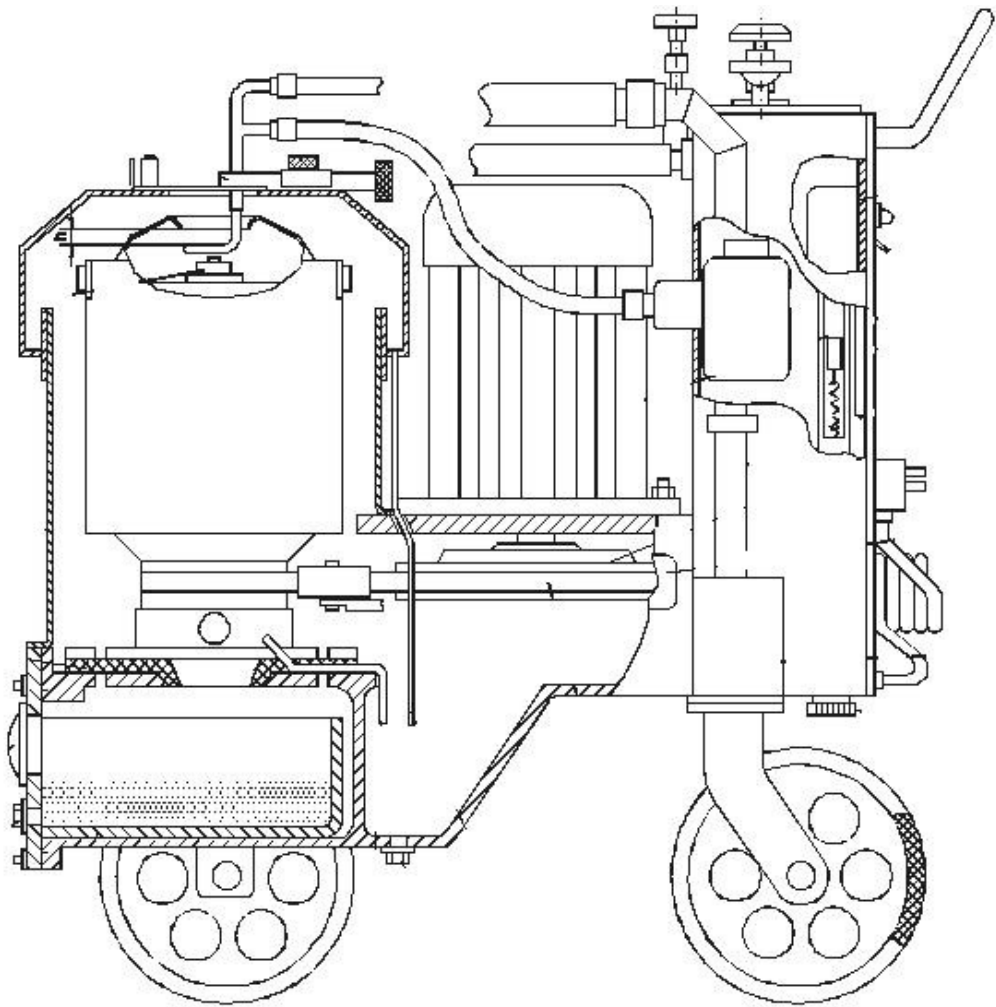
Габаритный чертеж стенда очистки жидкостей
